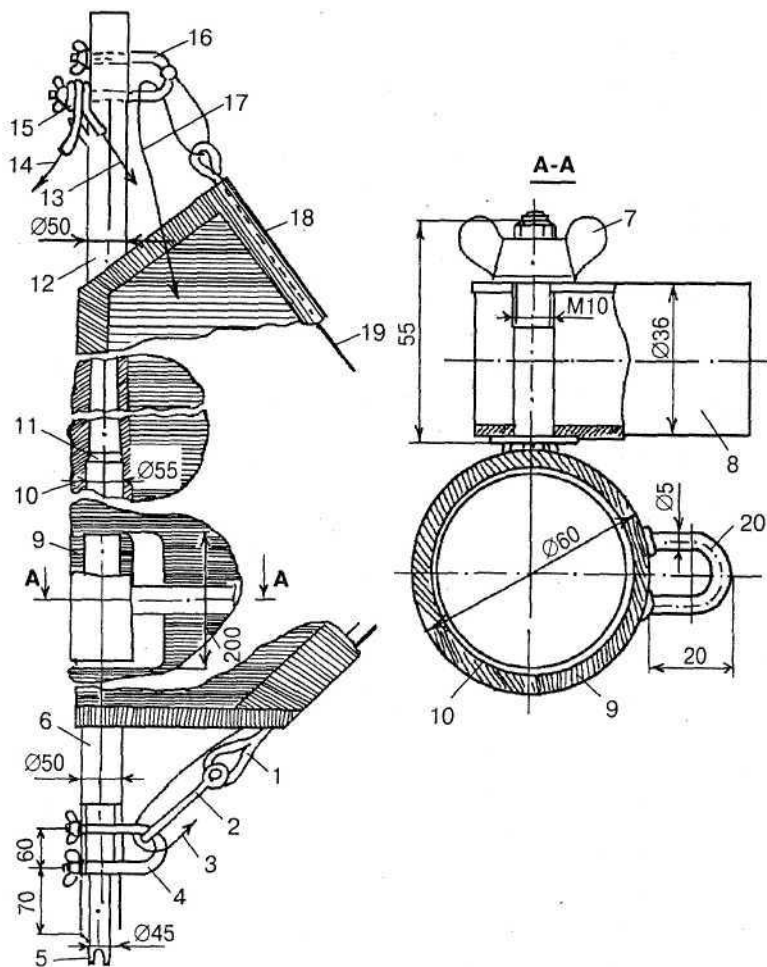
Мачта: 1 — сгон ликтроса нижней шкаторины; 2 — соединительная мочка; 3 — ходовой конец тали регулировки «пуза» паруса; 4 — нижняя скоба 08 мм; 5 — шпор мачты; 6 — нижнее колено мачты, труба 50x2, длина 1650 мм; 7 — гайка-барашек M10; 8 — гик; 9 — скользящая втулка гика; 10 — среднее колено мачты, труба 55x2, длина 1750 мм; 11 — упорная заклепка диам. 4; 12 — верхнее колено мачты, труба 50x1,5; длина 1750 мм; 13, 15 — ванты, 14 — штаг; 16 — верхняя скоба 08; 17 — ходовой конец фала; 18 — карман задней шкаторины; 19 — ликтрос; 20 — скоба проводки фала
